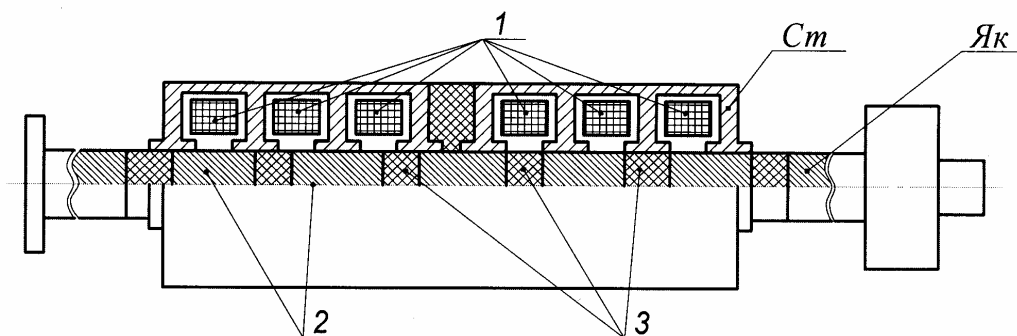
Принципова схема конструкції циліндричного лінійного крокового двигуна:
